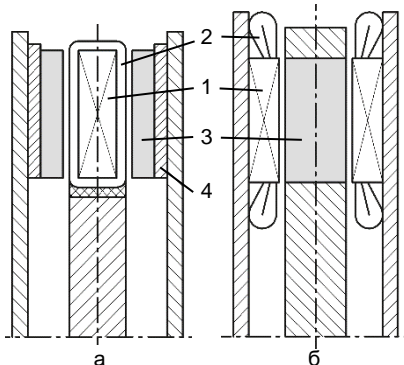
Конструкции торцевых генераторов с двойным рабочим зазором:
